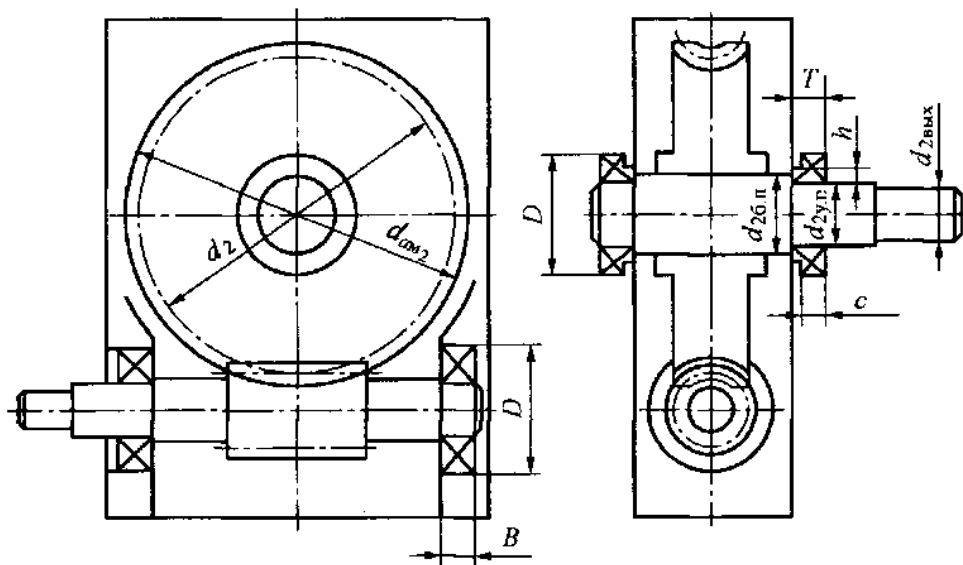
Эскиз вала редуктора и червячной передачи
